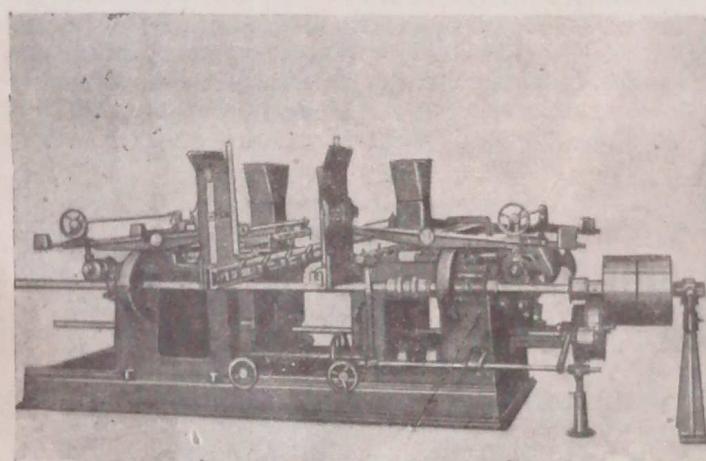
Двусторонний сверлильно-шкантозабивной станок с автоподачей (модель с ременным приводом)
